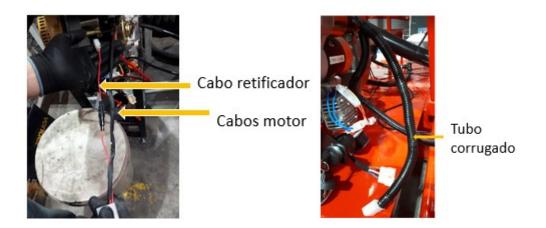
Cabo do motor e retificador e cabo de ignição 1° via envolvido com tubo corrugado
